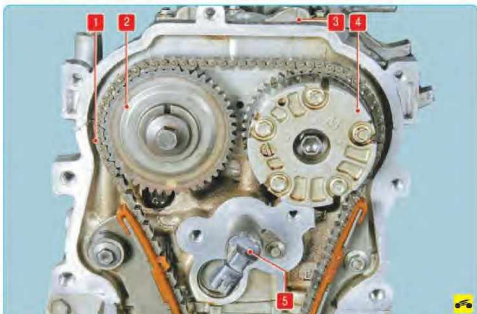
Элементы системы регулирования фаз газораспределения двигателя объемом 2,0 л: 1 – цепь привода газораспределительного механизма; 2 – звездочка впускного вала; 3 – крышка подшипников распределительных валов; 4 – механизм регулирования положения распределительного вала впускных клапанов; 5 – электромагнитный клапан системы регулирования фаз газораспределения
